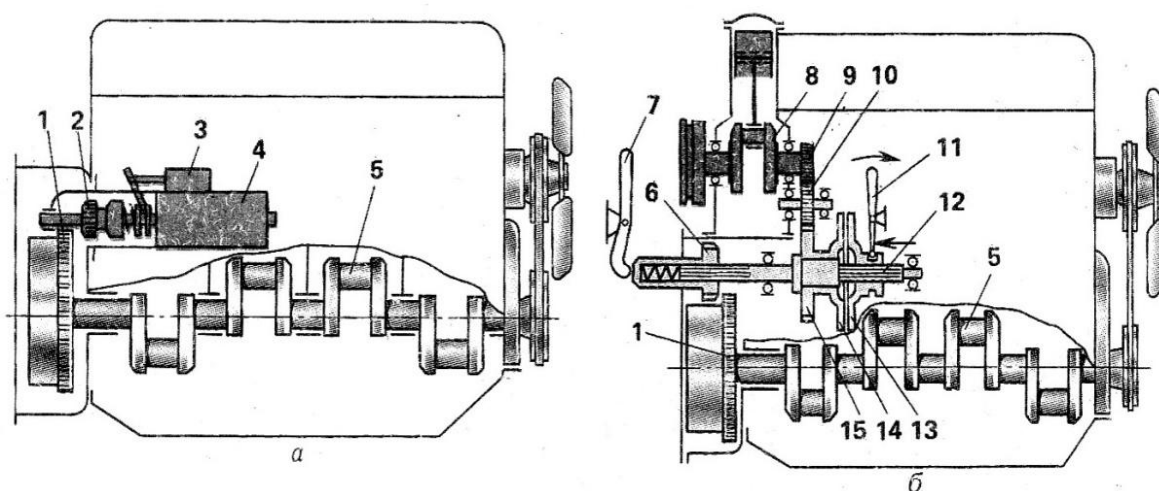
Схемы систем пуска: а – с электрическим стартером; б – с пусковым двигателем; 1 – зубчатый венец маховика; 2,6 – приводные шестерни; 3 – тяговое реле; 4 – электростартер; 5,8 – коленчатые валы; 7,11 – рычаги; 9,10,15 – шестерни; 12 – вал механизма передачи; 13,14 – диски сцепления
